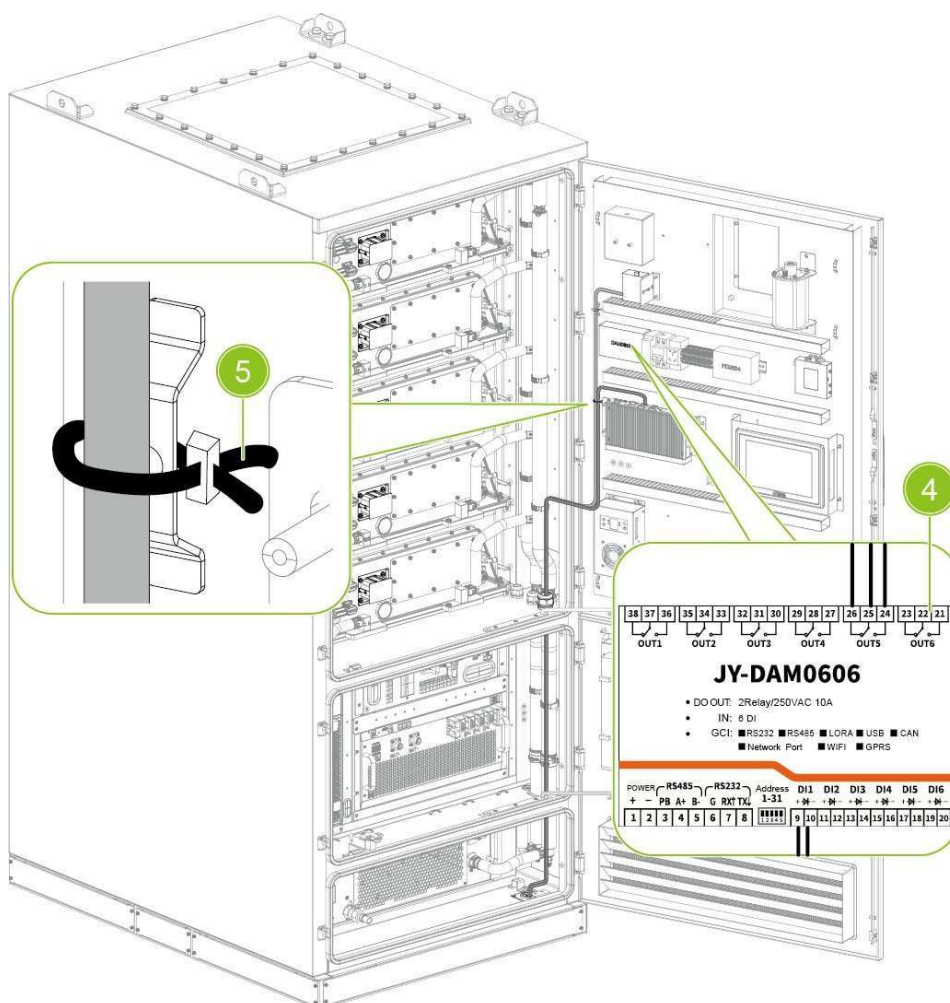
Conecta el cable al controlador e instala las abrazaderas
